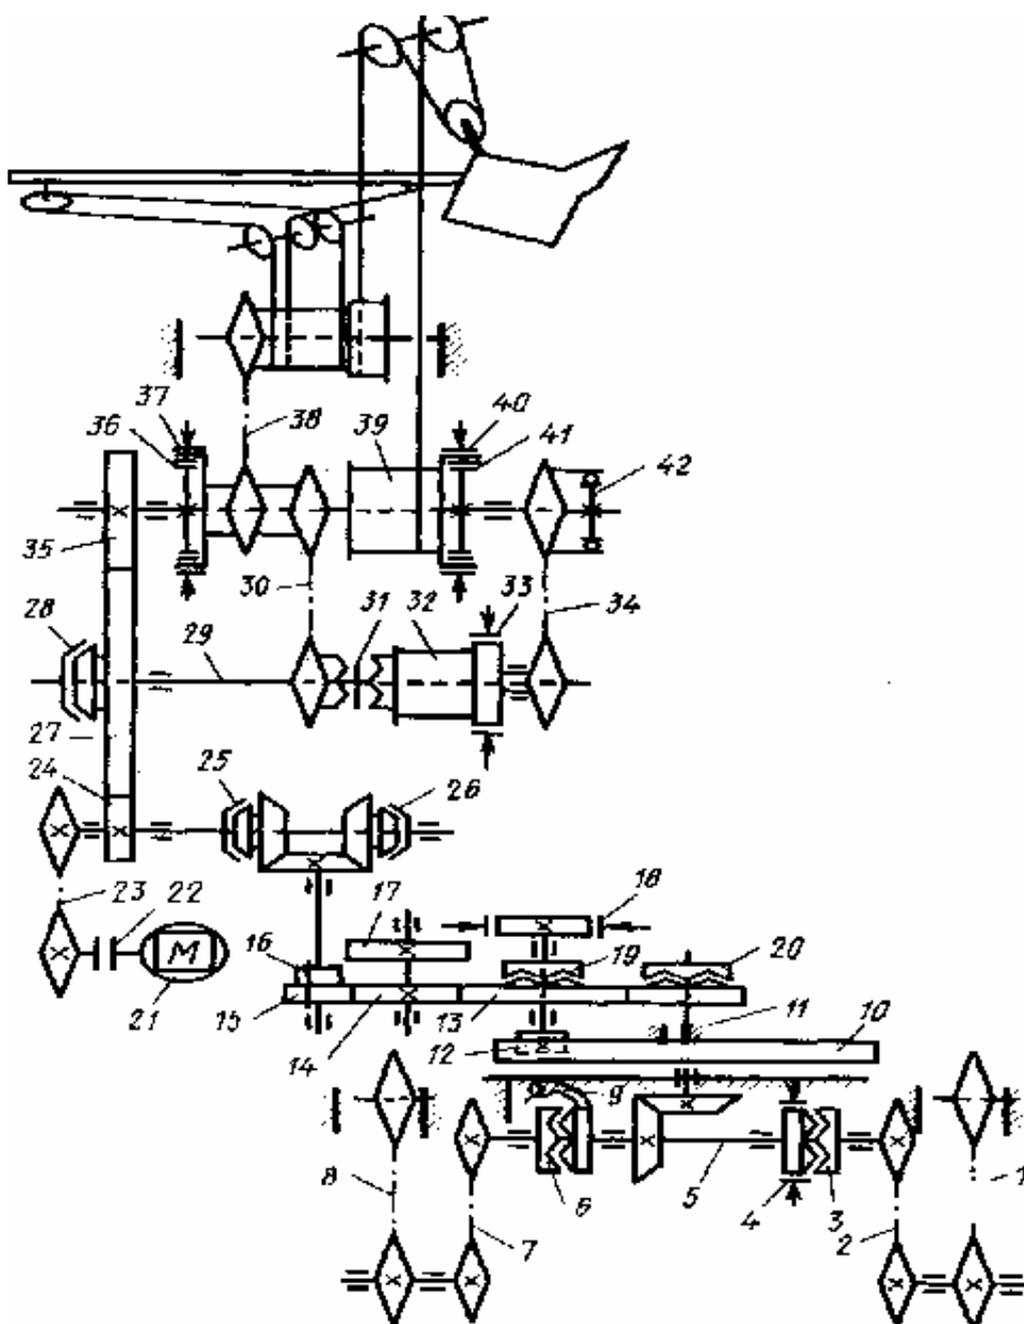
Кинематические схемы одноковшовых гусеничных экскаваторов с рабочим оборудованием прямая лопата.
